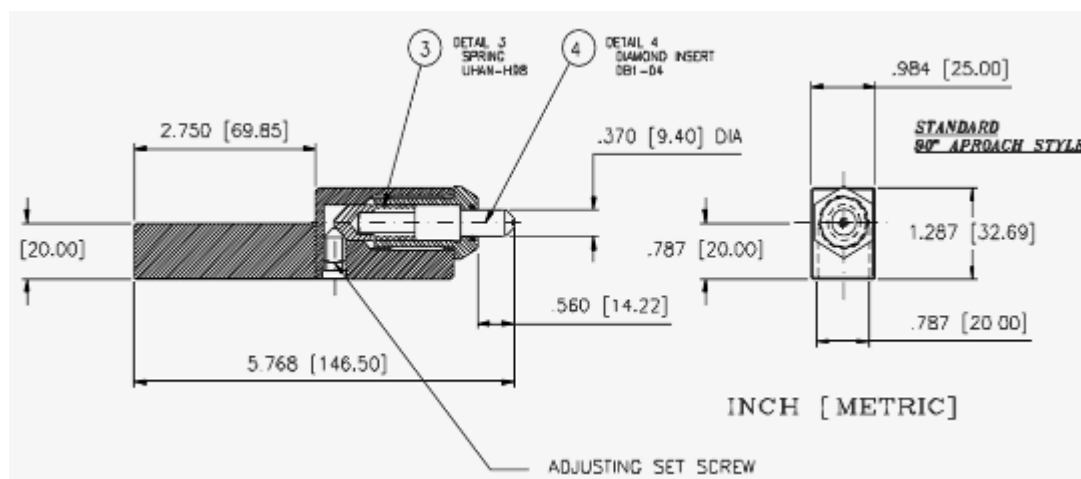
Инструмент DB-3 Cogsidill Tool
